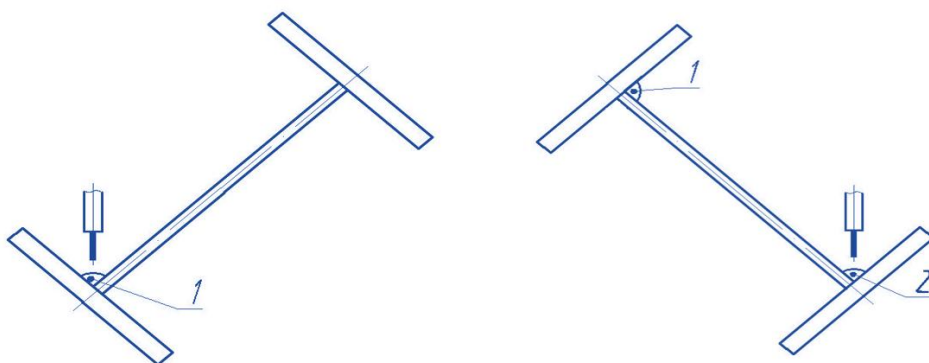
Порядок накладання швів при виготовленні гофрбалки
